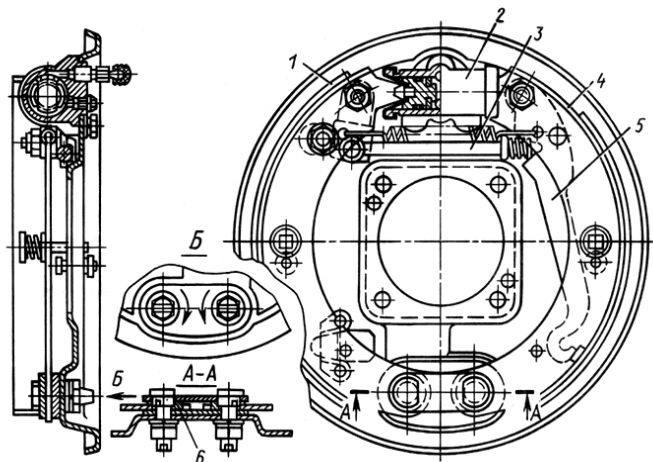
Конструкция тормозного механизма с одним цилиндром и фиксированными опорами колодок: 1 — передняя колодка; 2 — гидроцилиндр; 3 — толкатель стояночного тормоза; 4 — задняя колодка; 5 — рычаг стояночного тормоза; 6 — палец опоры колодки
